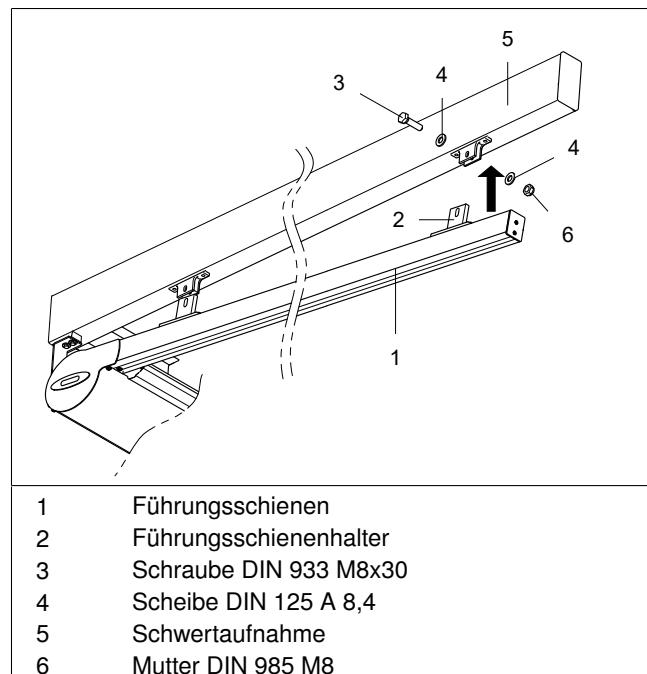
Führungsschiene befestigen (Abstandsmontage)
